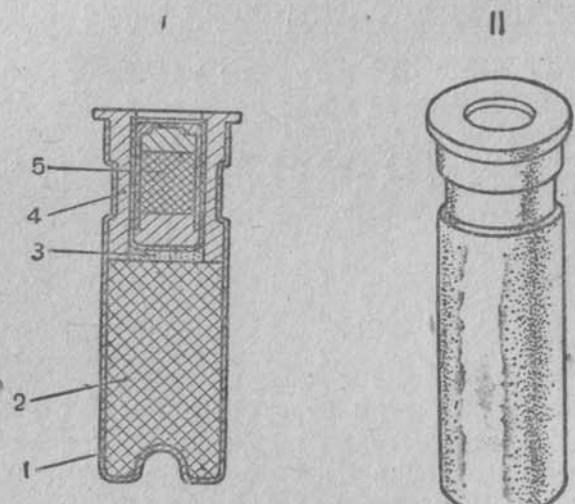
Запал: I — вид в разрезе; II — наружный вид:
